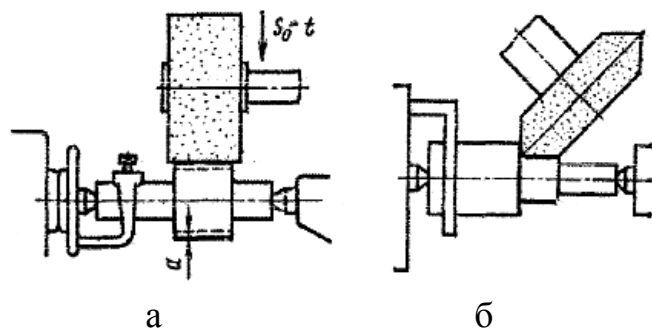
Схема круглого шлифования с поперечной подачей (а); схема шлифования шейки и уступа вала (б).
